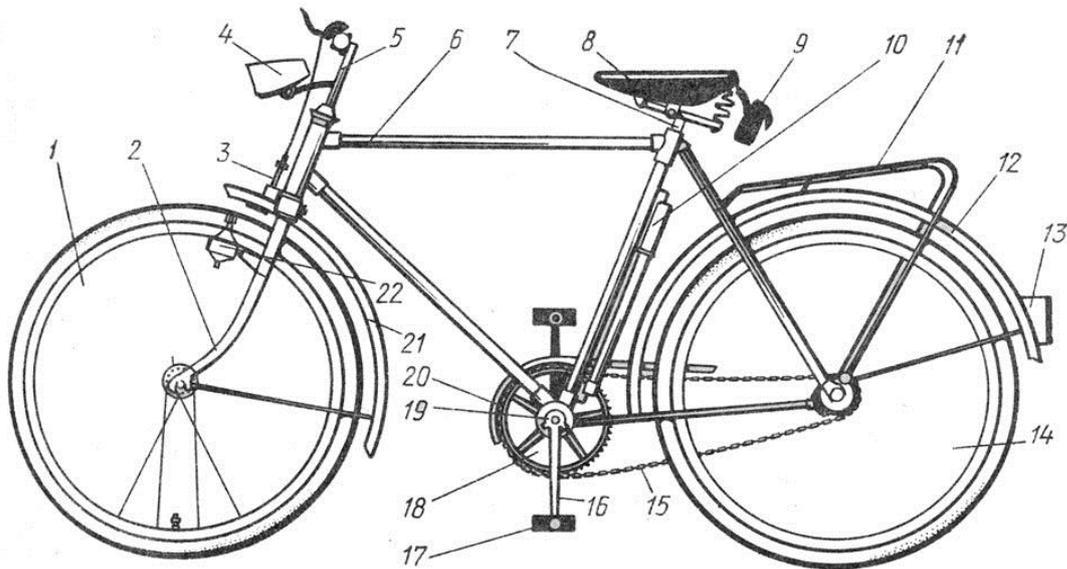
Основные узлы и детали велосипеда. 1 – переднее колесо; 2 – передняя вилка; 3 – тормоз переднего колеса; 4 – фара; 5 – руль; 6 – рама; 7 – седлодержатель; 8 – седло; 9 – сумка с инструментом; 10 – насос; 11 – багажник; 12 – щиток заднего колеса; 13 – задний фонарь; 14 – заднее колесо; 15 цепь; 16 – шатун; 17 – педаль; 18 – ведущая звездочка; 19 – каретка; 20 – щиток цепи; 21 – щиток переднего колеса; 22 – электрогенератор освещения.
